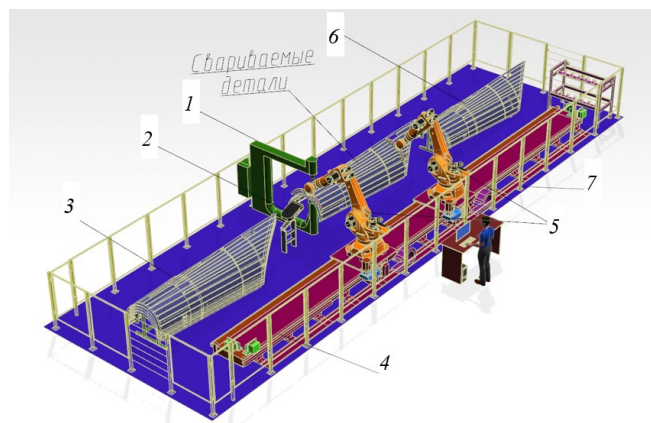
Роботизированный технологический комплекс сварки панелей
